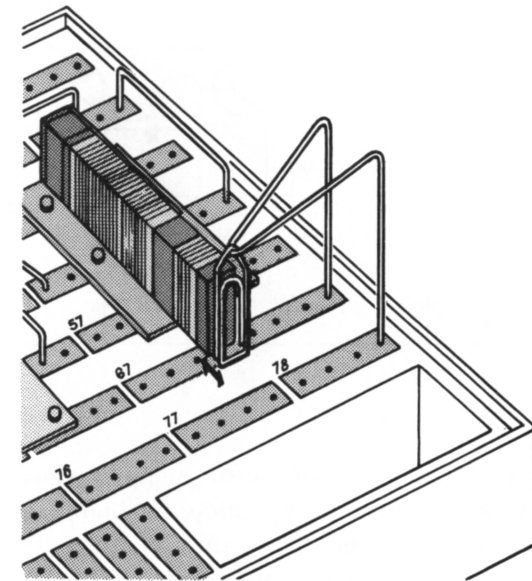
So wird die Büroklemme freischwingend an einem langen Drahtstück aufgehängt.
